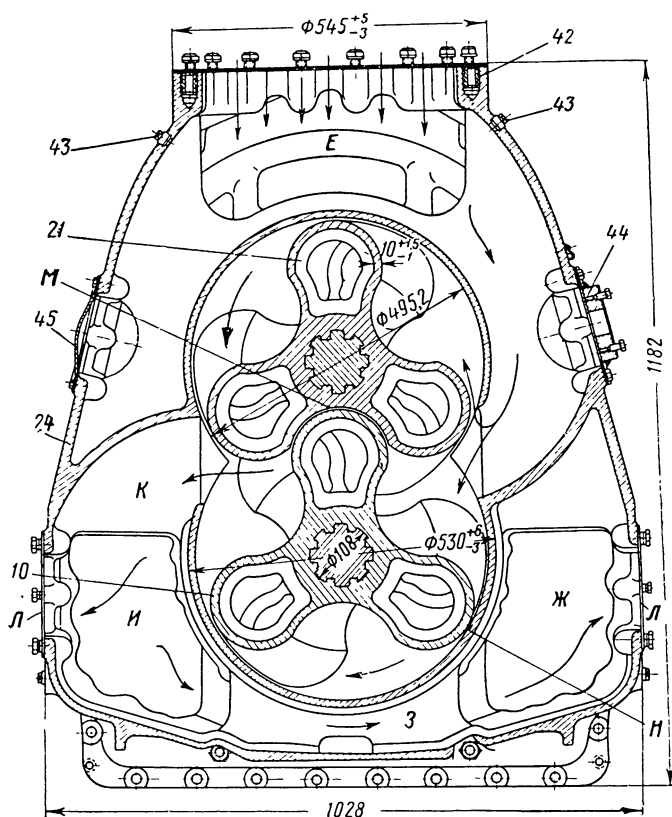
Поперечный разрез воздуходувки (обозначения см. на рис. 57):
